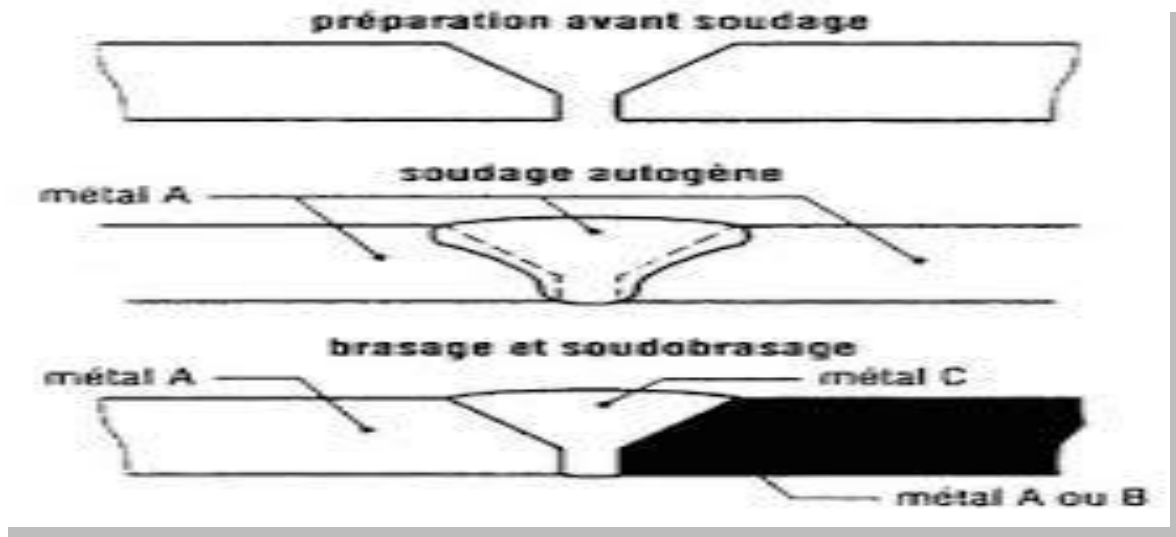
Assemblage de deux pièces par soudage.
